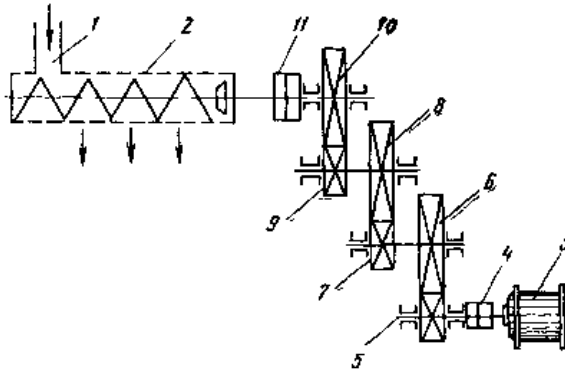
Кінематична схема форпреса ФП: 1 – жолоб для мезги; 2 – зерний циліндр; 3 – електродвигун; 4 – муфта зчеплення; 5 – вал-шестерня; 6, 7, 8, 9, 10 – шестерні; 11 – запобіжна муфта
